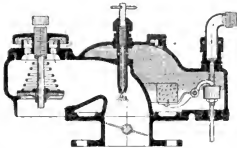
Dreizylinder-Ferro-Motor. Vergaser.
